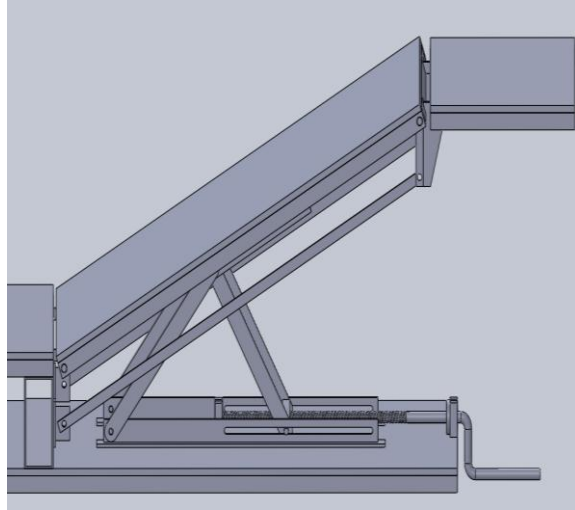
Sistema proposto de levantamento do dispositivo
